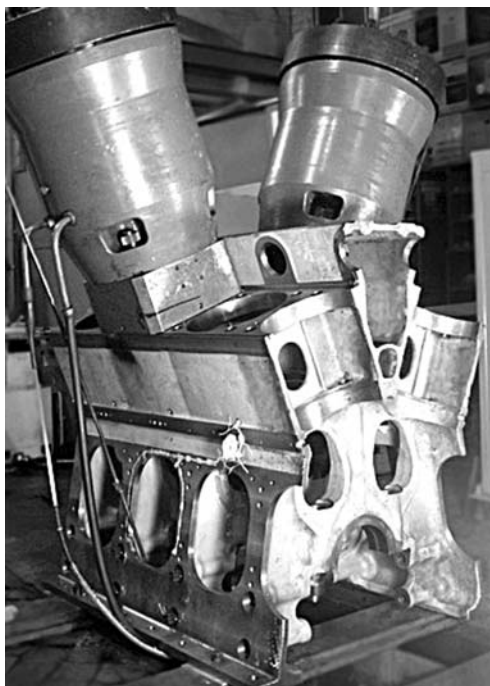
Стенд для усталостных испытаний блока цилиндров дизеля 16ЧН26/26
